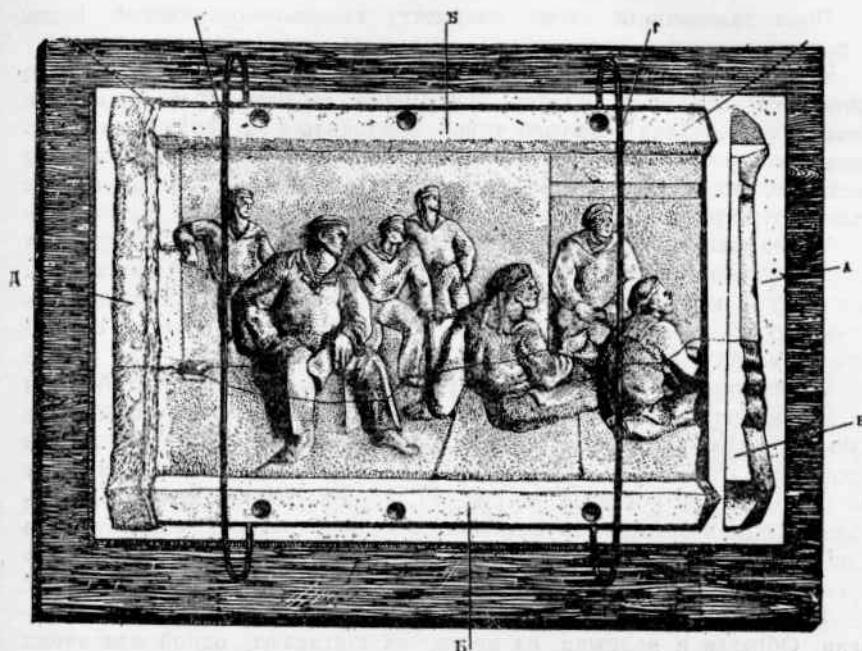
Формовка простого рельефа. А — плоскость (грунт), на которой укреплен рельеф. Б — боковые куски по длинным сторонам рельефа. В — торцовые концы боковых кусков. Г — скобки. Д — короткий боковой кусок, не обрезанный. Е — короткий боковой кусок, обрезанный.
